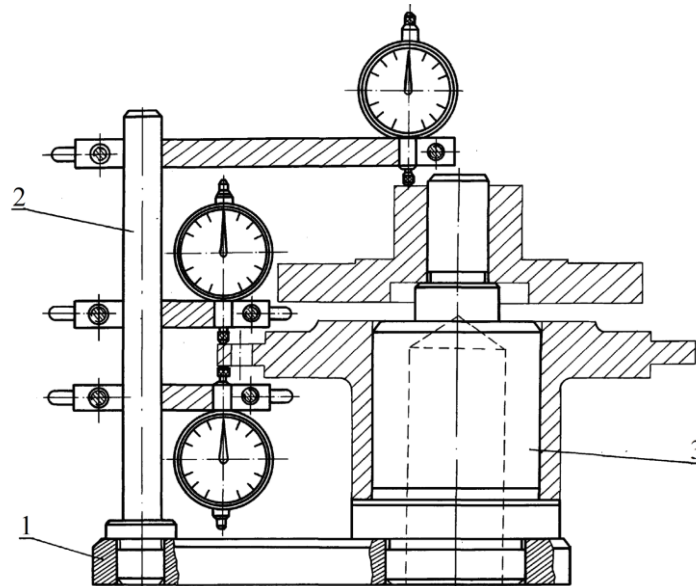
Багатовимірний контрольно-вимірювальний пристрій
